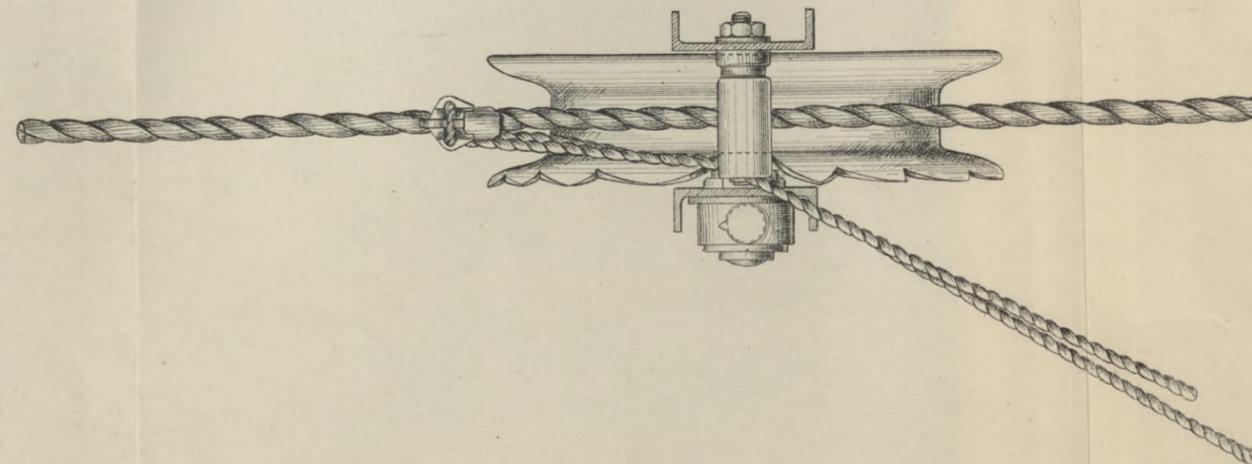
PLAN. OBLIQUITÉ DE L'AMARRE
